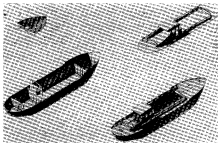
Некоторые типы сборки корпуса грузового теплохода.
